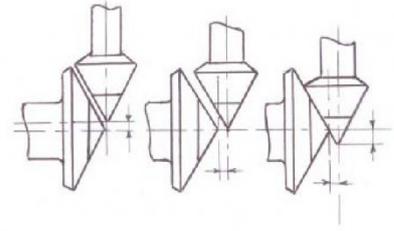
Несовпадение вершин делительных конусов конических зубчатых колес при сборке передач
